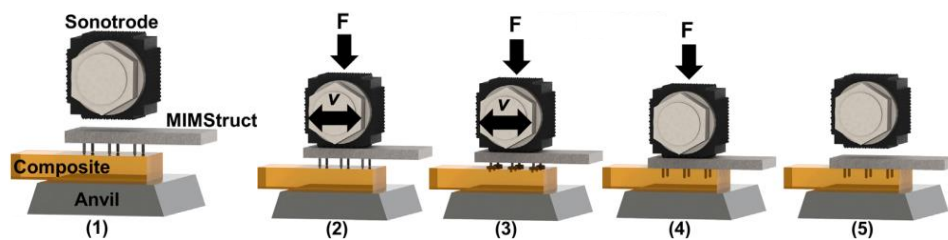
Phases d'assemblage du procédé U-Joining [51]
